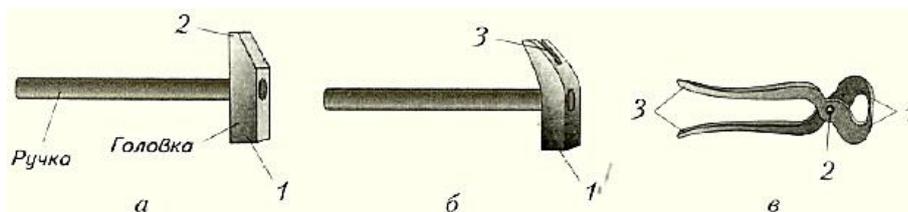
Столярные инструменты: а, б – молотки: 1 – боёк; 2 – носок; 3 – прорезь для вытаскивания гвоздей; в – клещи: 1 – губки; 2 – ось; 3 – ручки
